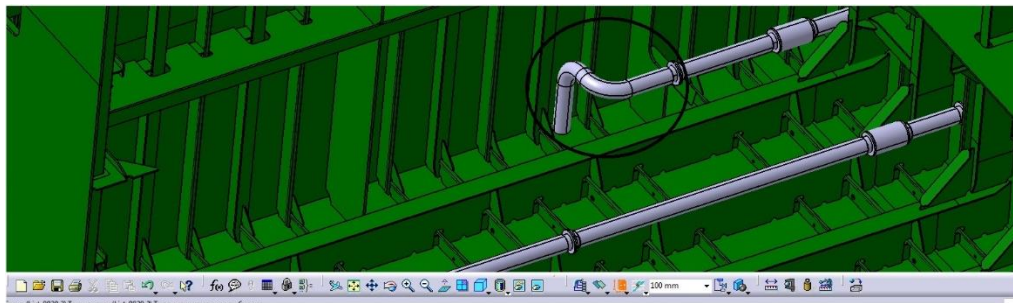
Труба с координатами для гибки на станке с ЧПУ
